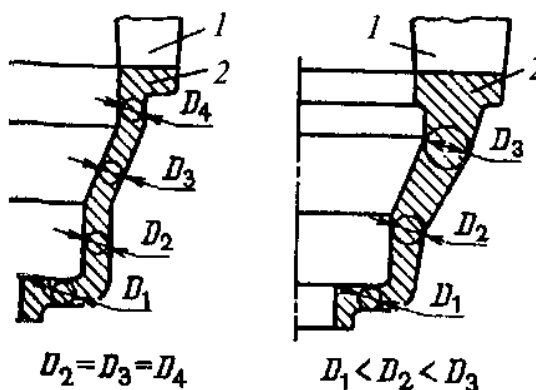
Конструкции литых деталей, обеспечивающих одновременное (а) и направленное (б) затвердевание отливок: 1 - прибыль; 2 — отливка
